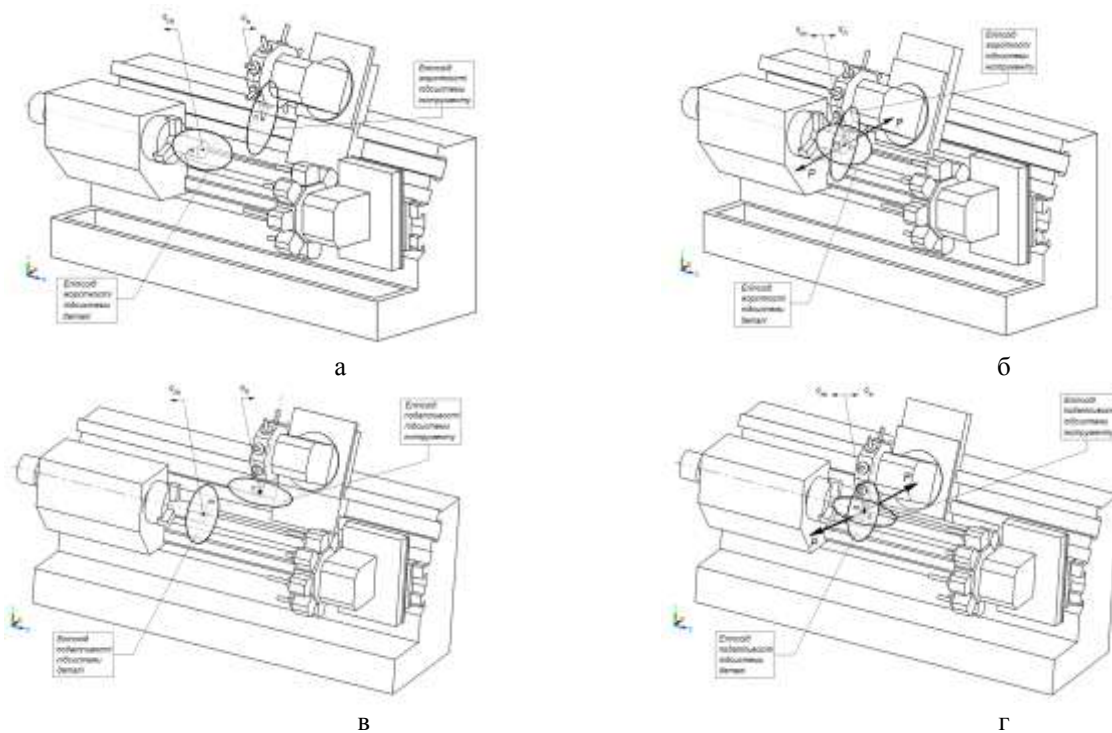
Конструктивні схеми ПС токарного верстату з еліпсоїдами жорсткості (а, б) та податливості (в, г): а, в - в неробочому стані; б, г - в робочому стані (при різанні)
